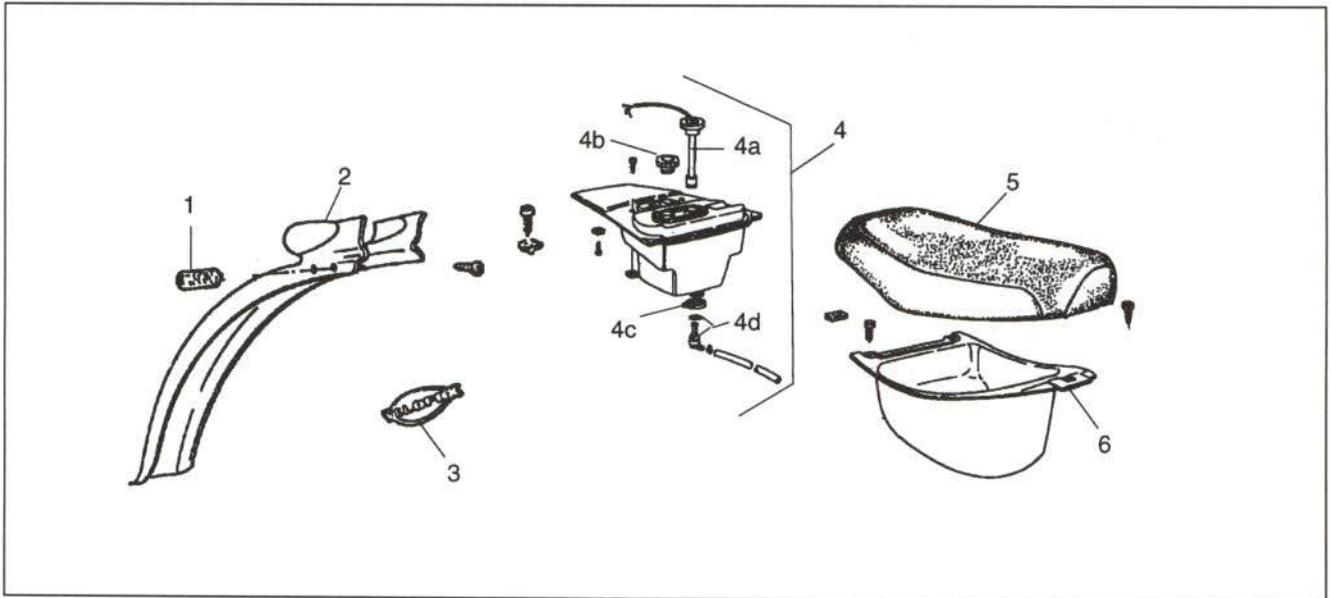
Despiece de las piezas exteriores de la parte trasera
